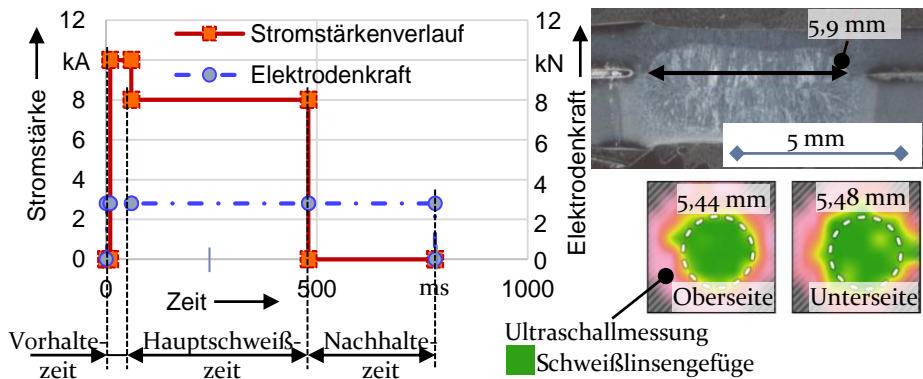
Schweißparameter und resultierender Schweißlinsendurchmesser
